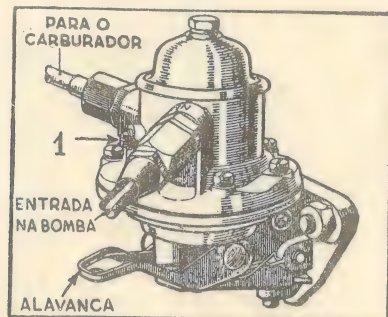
Bomba de gasolina com filtro sob a tampa
